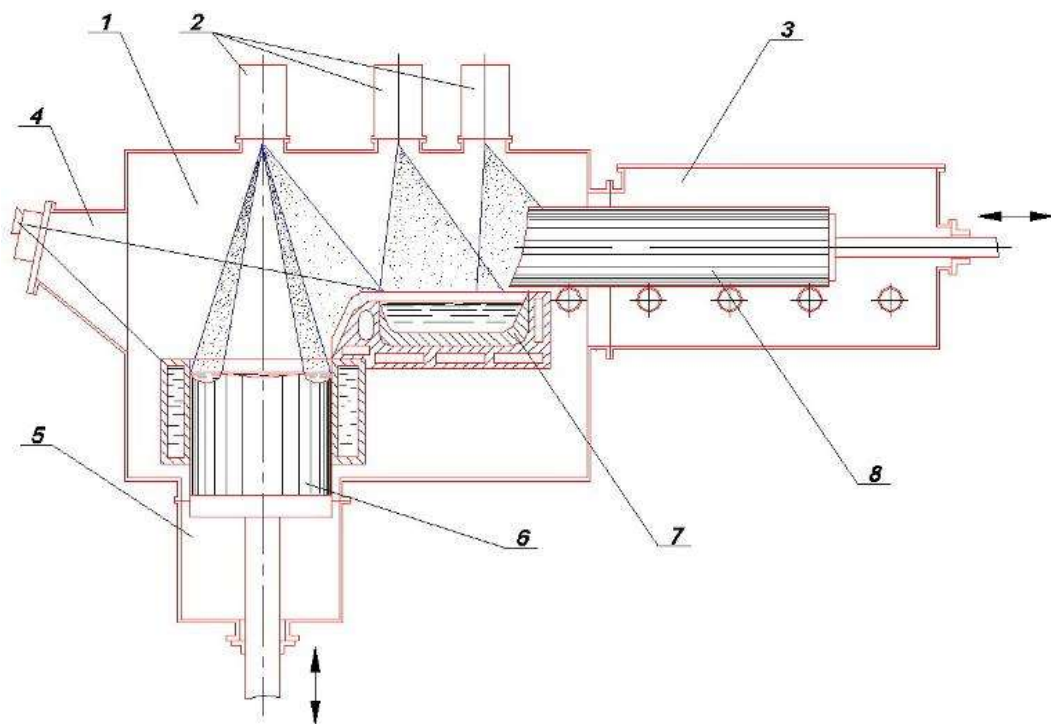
Схема установки УЕ-5810: 1-камера плавки, 2-електронні гармати, 3-камера заготовки, 4 - оглядова система, 5-камера зливка, 6-зливоч, 7-проміжна ємність, 8-шихтова заготовка
